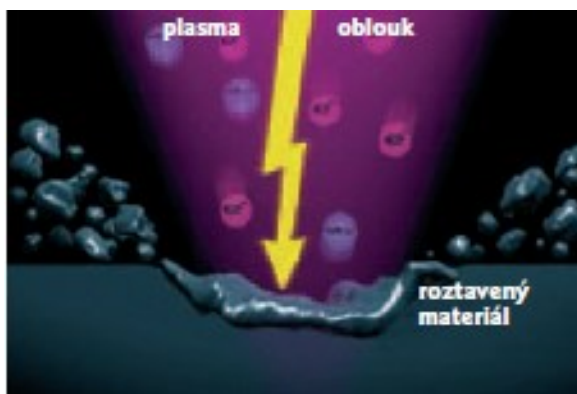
Oblouková technologie s rotačními elektrodami [3]
